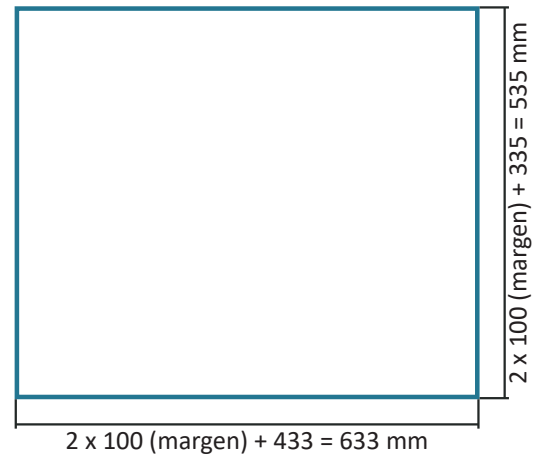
Planta de la pieza (paso entre columnas)
